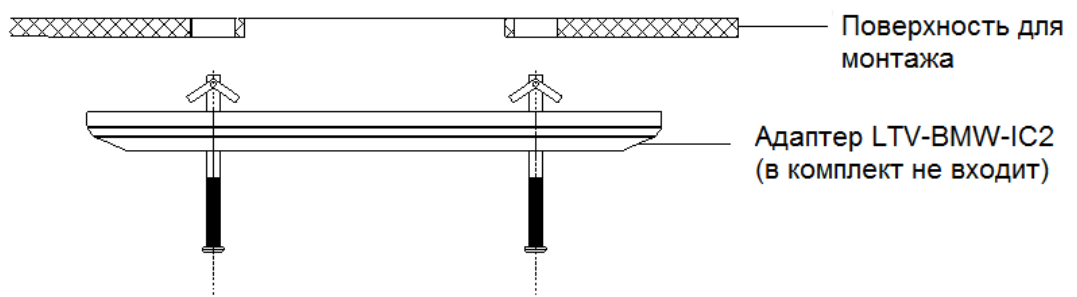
Крепление адаптера LTV-BMW-IC2 на потолок / стену
